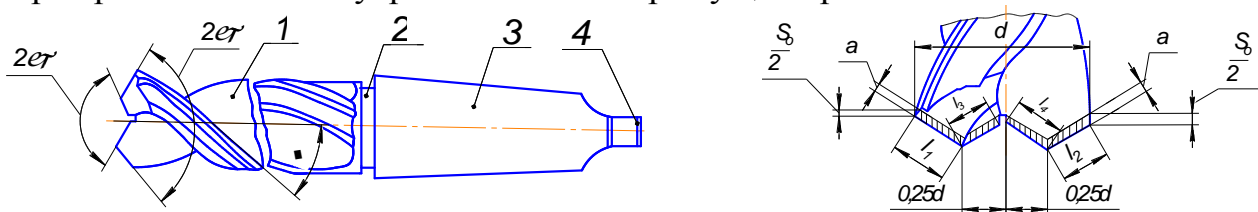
Двухвершинное спиральное сверло без поперечной кромки с направляюще-выглаживающими ленточками
